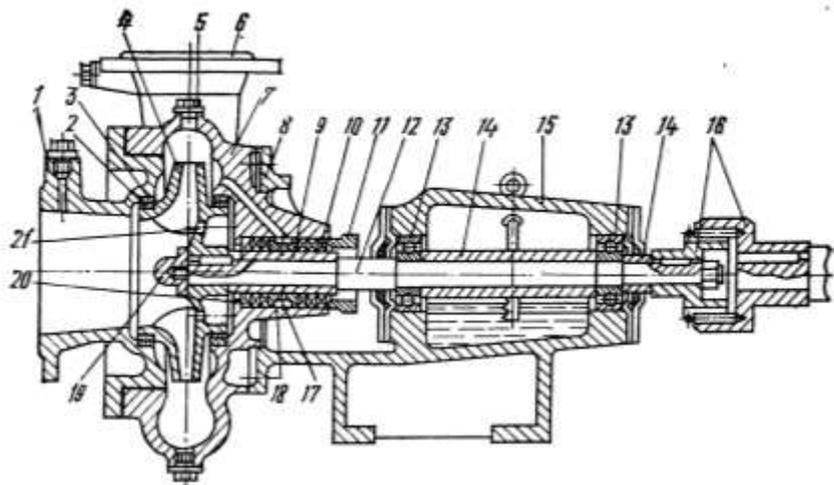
Конструкция консольного горизонтального центробежного насоса: 1, 6 — всасывающий и напорный патрубки; 2, 3, 17 — кольца соответственно уплотняющее, защитное, гидравлического уплотнения; 4 — рабочее колесо; 5 — пробка; 7 — корпус насоса со спиральным отводом; 8 — кронштейн; 9, 14 — защитная и распорная втулки; 10 — сальниковая набивка; 11, 18 — подвижной фланец и корпус сальникового узла; 12 — вал; 13 — шарикоподшипники; 15 — опорная стойка с масляной ванной; 16 — полумуфты; 19 — гайка; 20 — фундамент; 21 — разгрузочное отверстие
